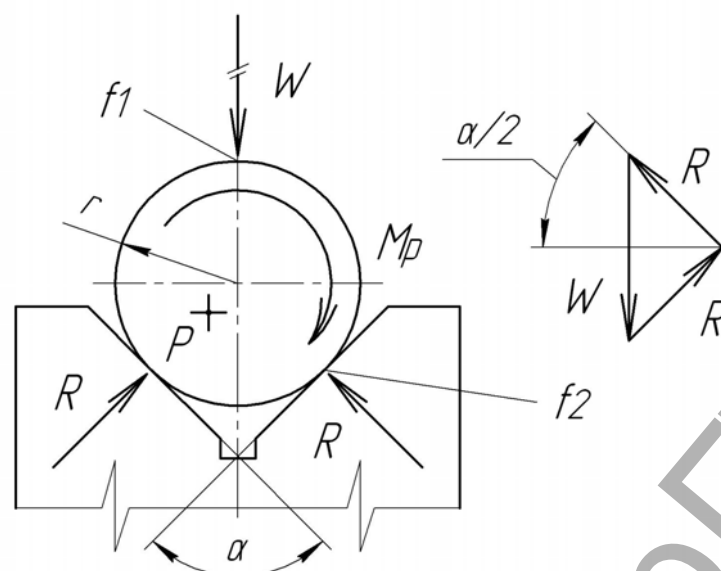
Схема сил, действующих на заготовку при ее установке в призму
